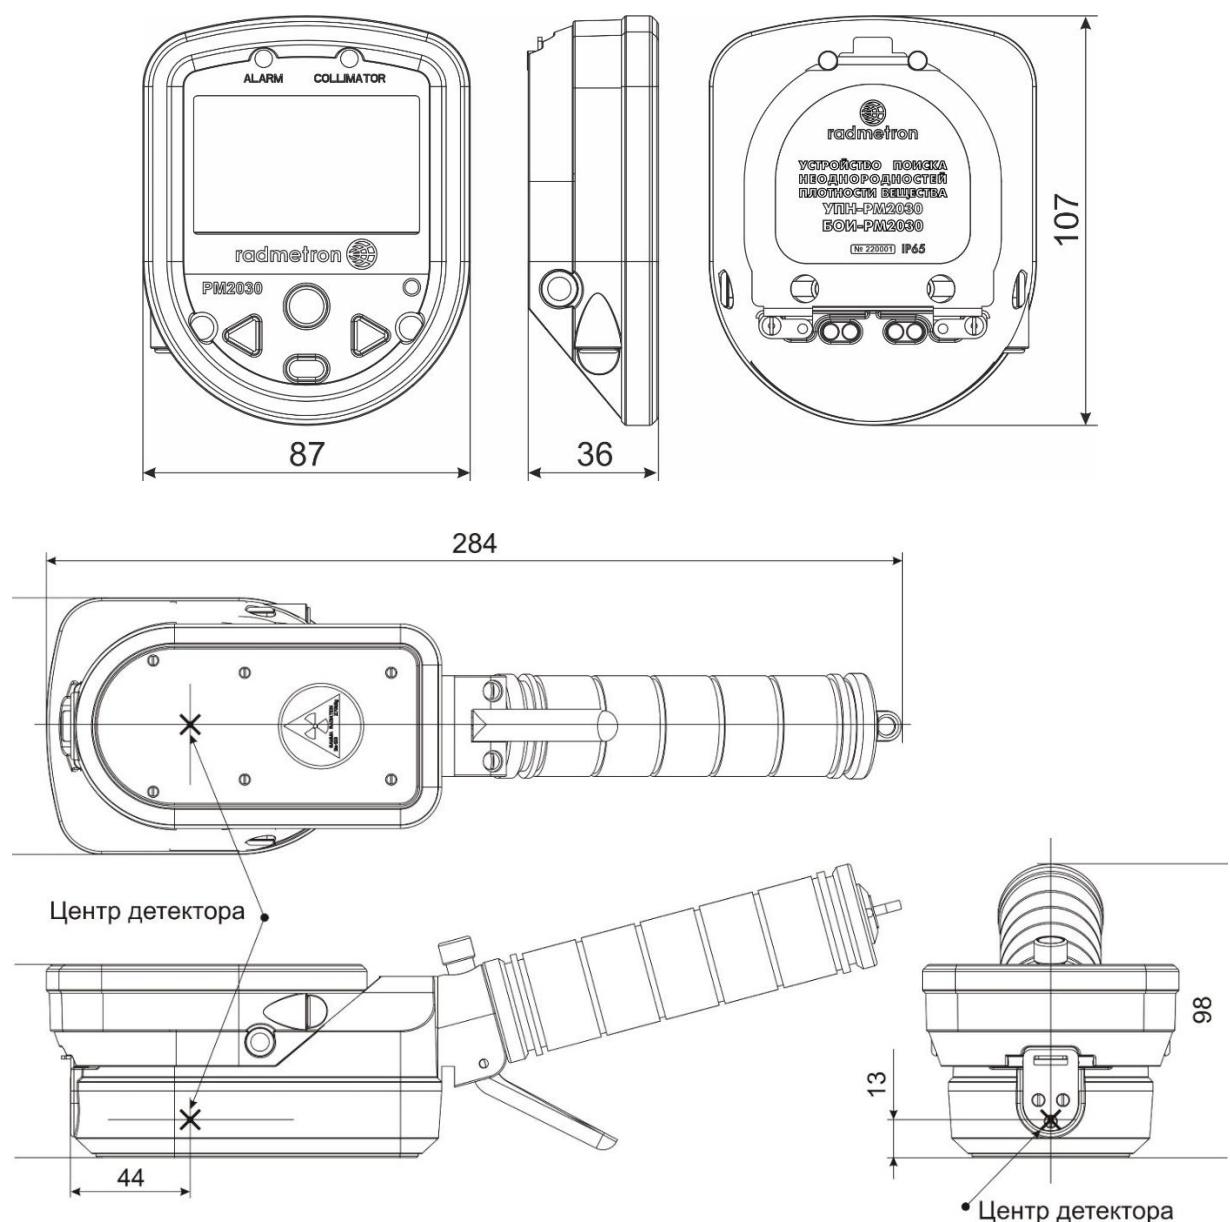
Габаритные размеры и геометрический центр детектора прибора
